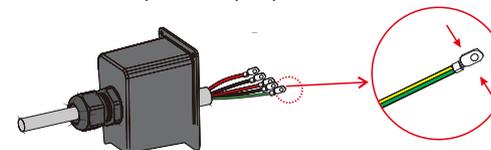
Установка соединительных клемм переменного тока
